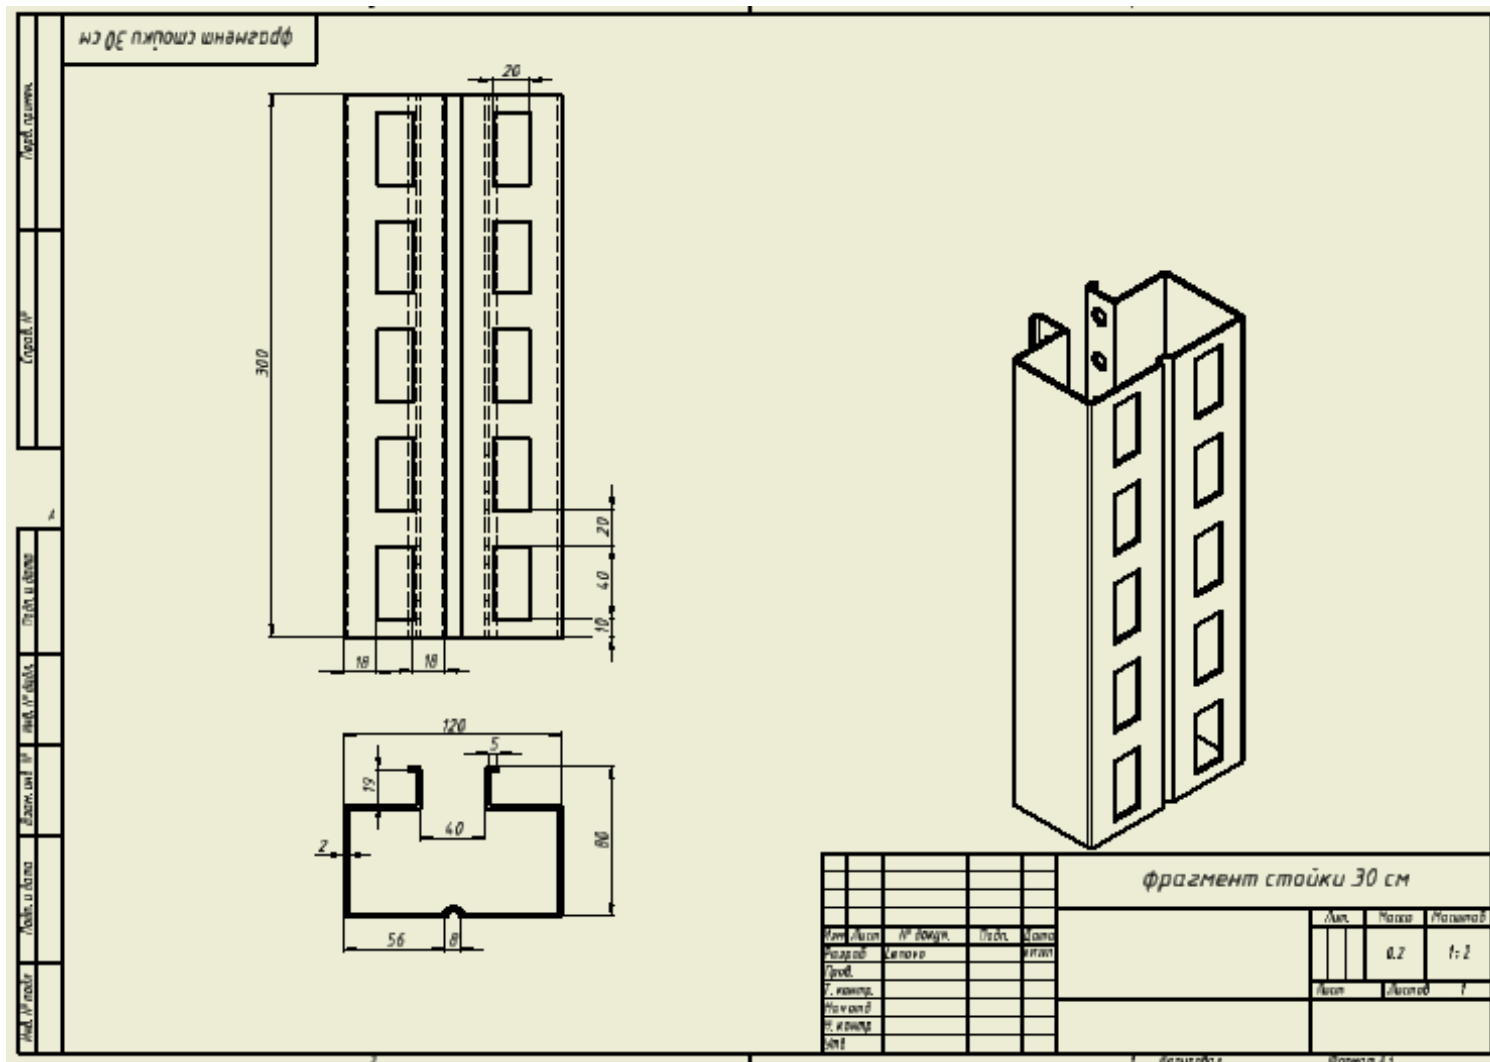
Креслення фрагмента стійки 300 мм.
